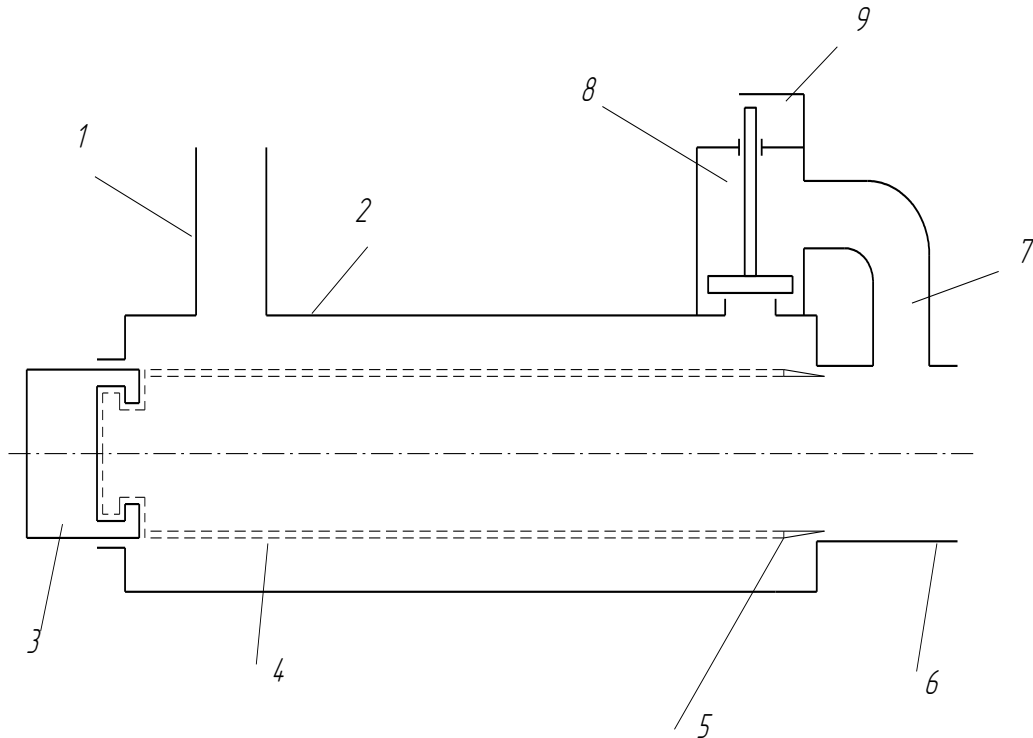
Схема молочного вакуумного фільтра : 1-вхідний патрубок; 2- корпус; 3-пробка;4- елемент, що фільтрує; 5 - кільце; 6-вихідний патрубок; 7 - обвідний патрубок; 8-клапан; 9-контакти.
